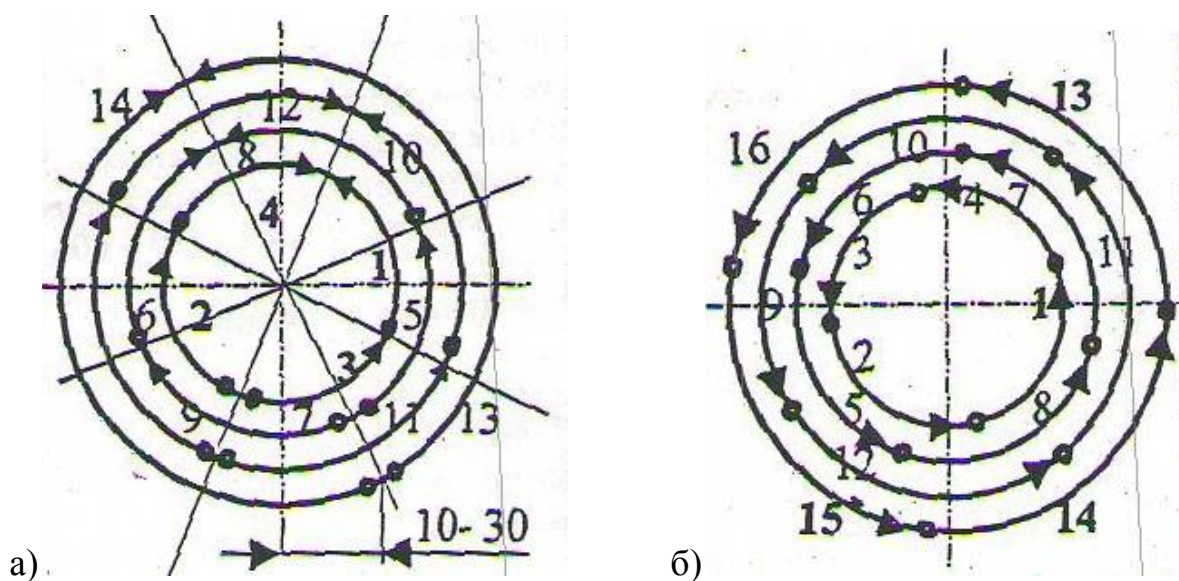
Порядок наложения слоёв при сварке вертикального стыка (а) и сварке горизонтального стыка (б)
